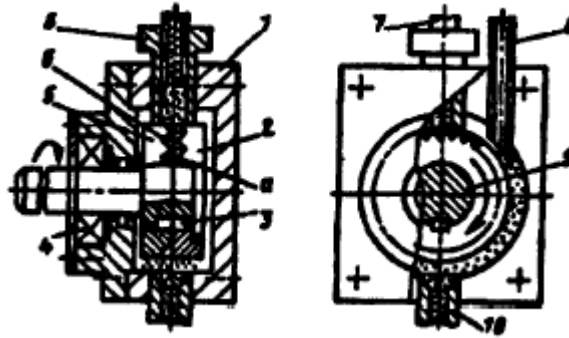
Живильник барабанного типу: 1 – корпус; 9, 5 – диски; 3 – шпонка; 4 – підшипник; 3, 8,10 – патрубки; 7 – трубка; 9 – вал; а, б – канавки.
